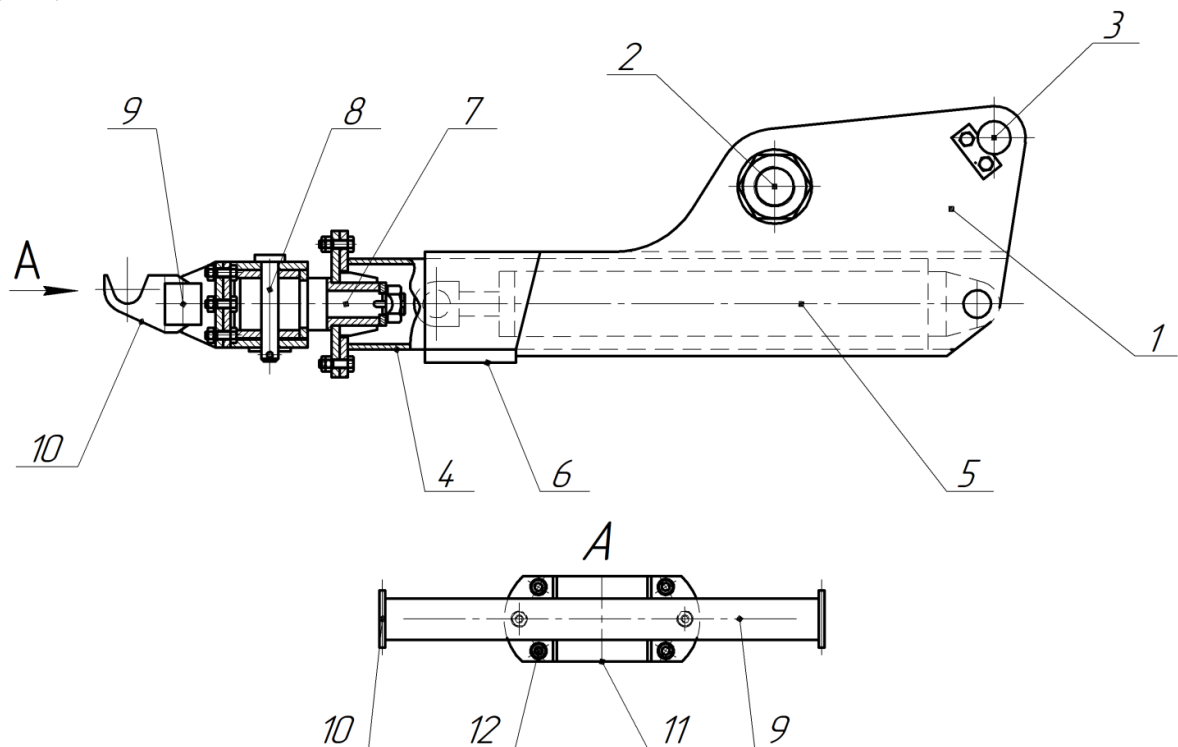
Конструктивна схема поворотної консолі телескопічного типу: 1 – рама; 2 – палець поворотного шарніра; 3 – палець; 4 – рама висувної консолі; 5 – гідроциліндр; 6 – підсилююча пластина; 7 – поворотний шарнір;
